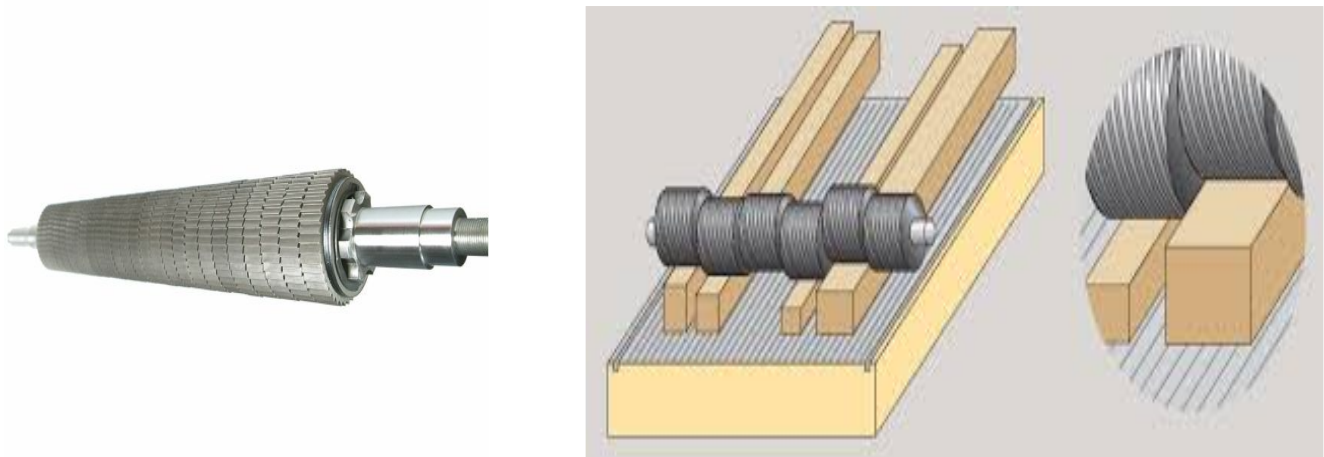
Робота секційного переднього валу механізму подачі рейсмусного верстата.
